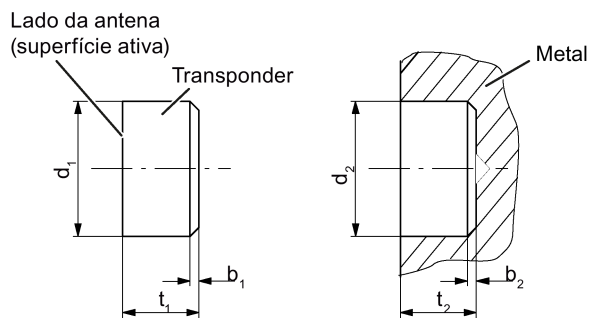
Montagem do MDS D521 encastrado em metal para ferramentas
